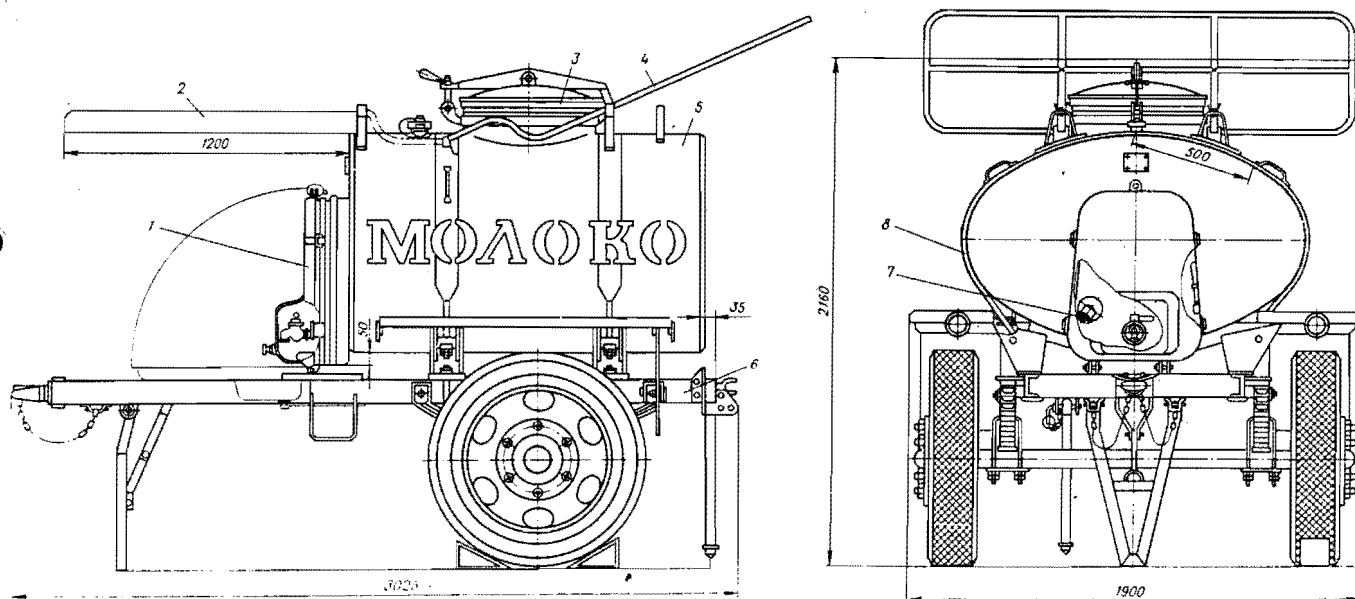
Общий вид прицепа-цистерны марки Р9-ОТВ-1,0:
